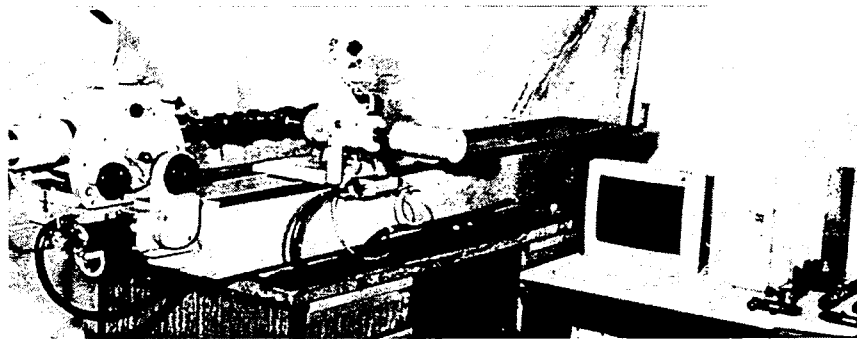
Полуавтоматическая установка КИП-2 для контроля кулачковых и коленчатых валов
